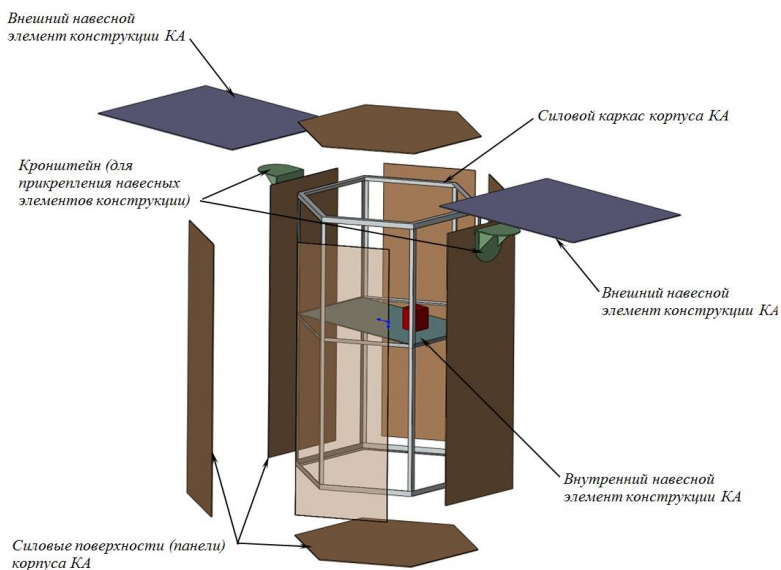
Пример, показывающий основные элементы конструкции КА
